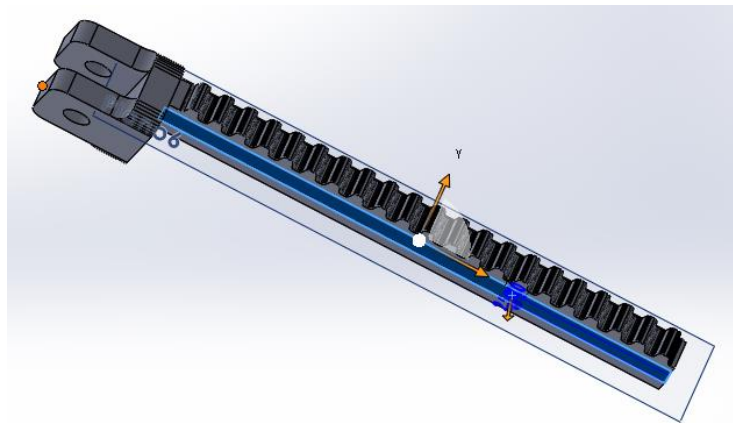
Diseño de los dientes que soportan el movimiento de los engranajes.
